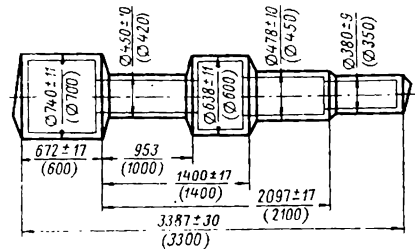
Пример чертежа поковки круглого сечения с уступами и выемками
